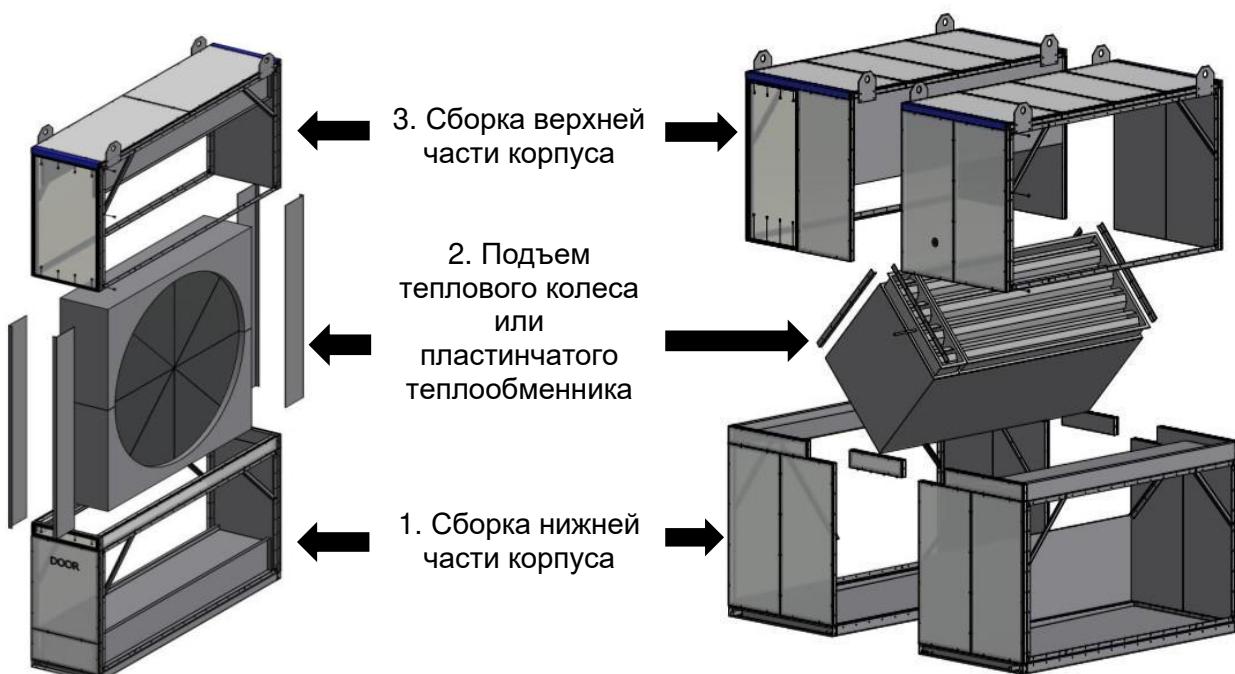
порядок сборки разобранный секции корпуса теплового колеса или пластинчатого теплообменника
